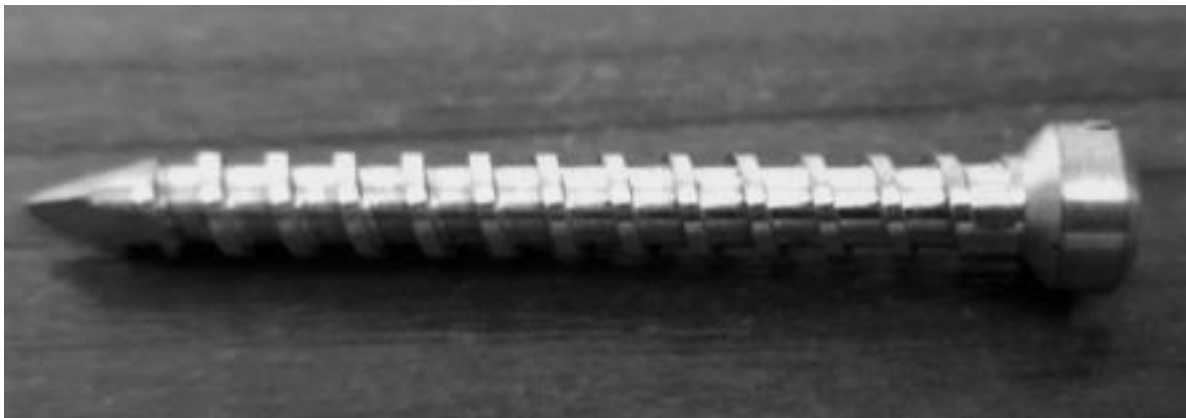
Винт, изготовленный из магниевого сплава МС-10
